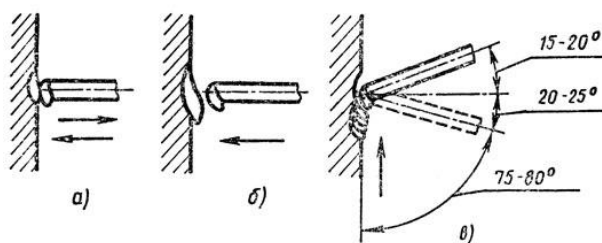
Схема техники выполнения наплавки валиков и вертикальных швов на подъем: а - зажигание дуги, б - образование сварочной ванны, в - движение электрода
